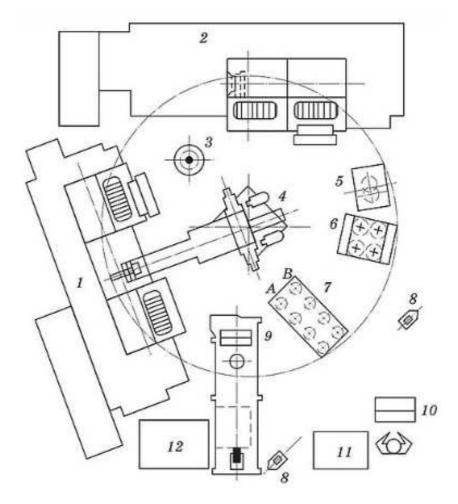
Схема ГПЯ (1 — токарный станок с ЧПУ, 2 — многоцелевой токарный станок, 3 — кантователь, 4 — промышленный робот, 5 — моечная машина, 6 — паллета с обработанными деталями, 7 — паллета с заготовками разного типа, 8 — защитное устройство, 9 — установка распознавания заготовок, 10 — пульт управления, 11 — монитор, 12 — система управления)
